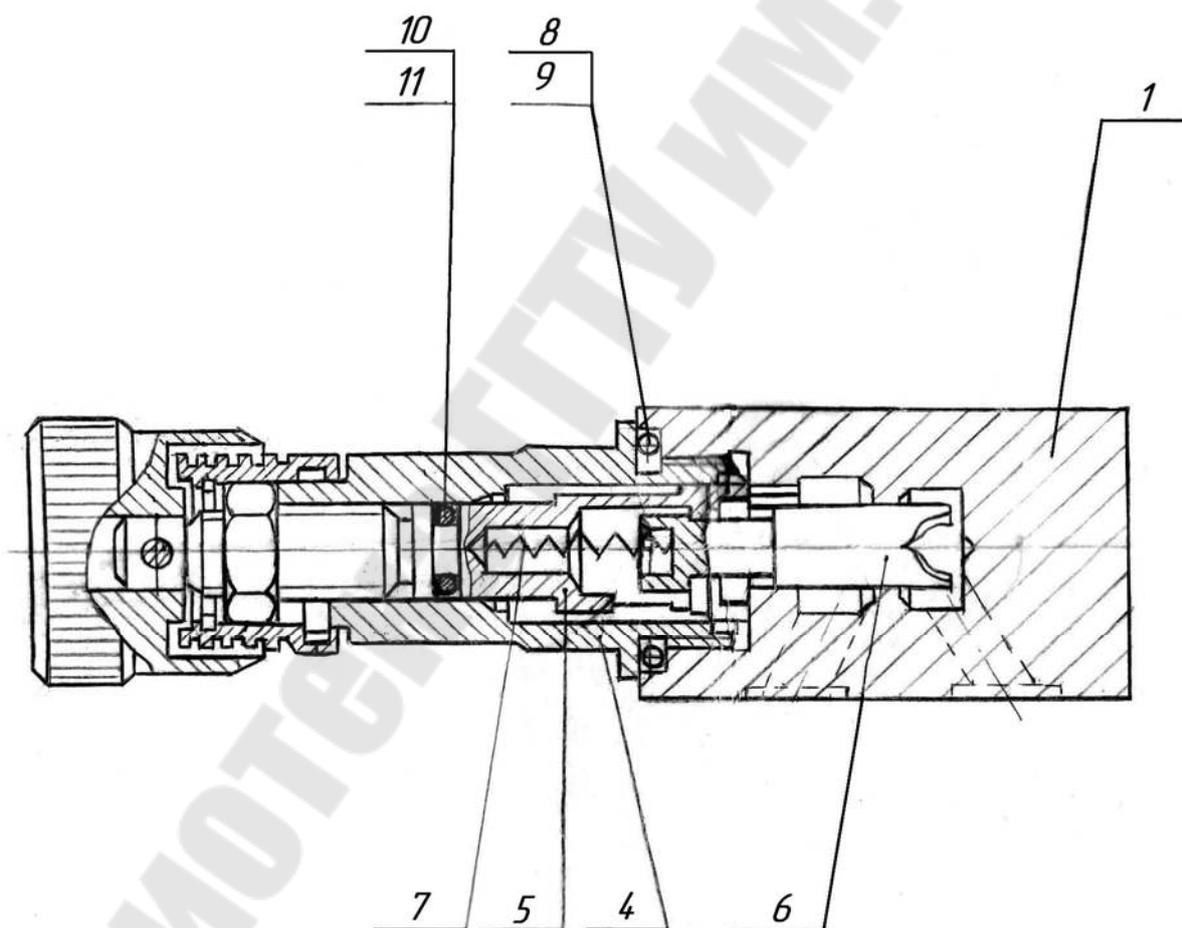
Конструкция блока присоединительного дросселя БПВ-...ДР
